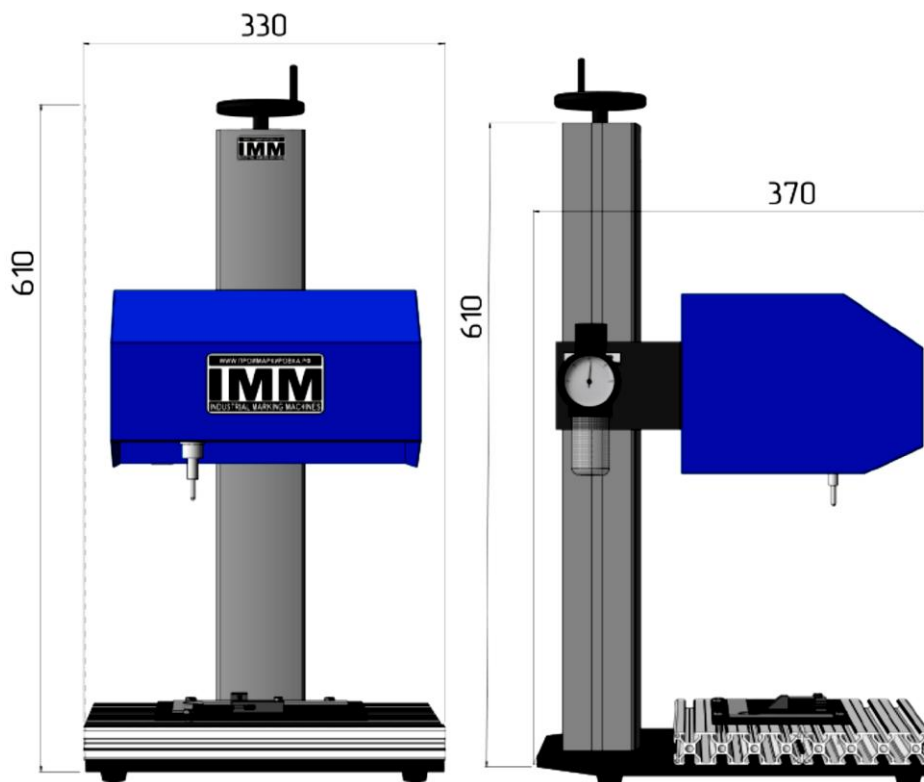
Пресове обладнання IMM-09TSH-170x100
